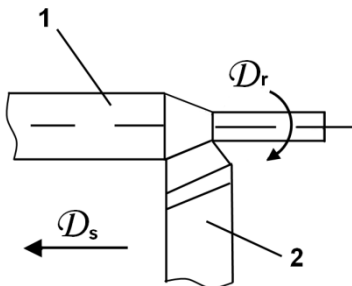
Точіння: 1- різець, 2- заготовка
